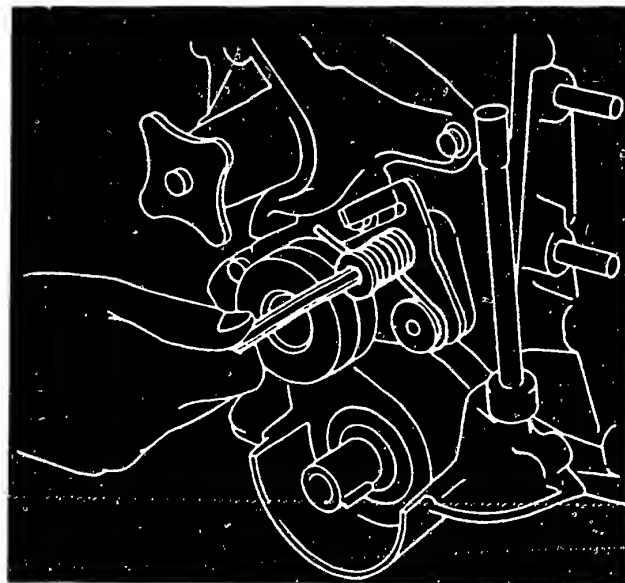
Vor dem Befestigen des Riemenspanners ist das Gewinde des Stehbolzens mit Haft-Dichtmittel zu bestreichen.
